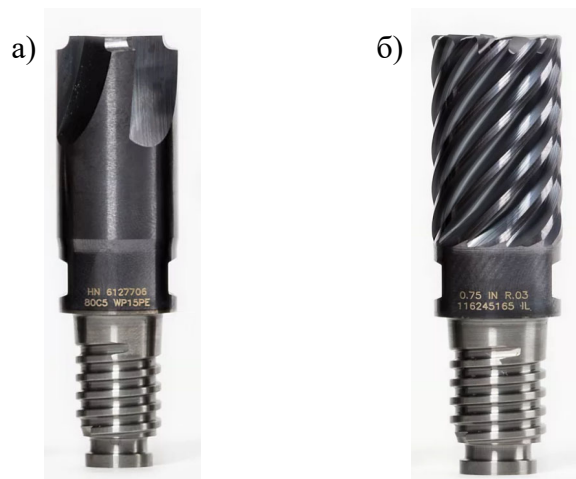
Твердосплавные концевые фрезы: а – с четырьмя зубьями, б – с девятью зубьями
